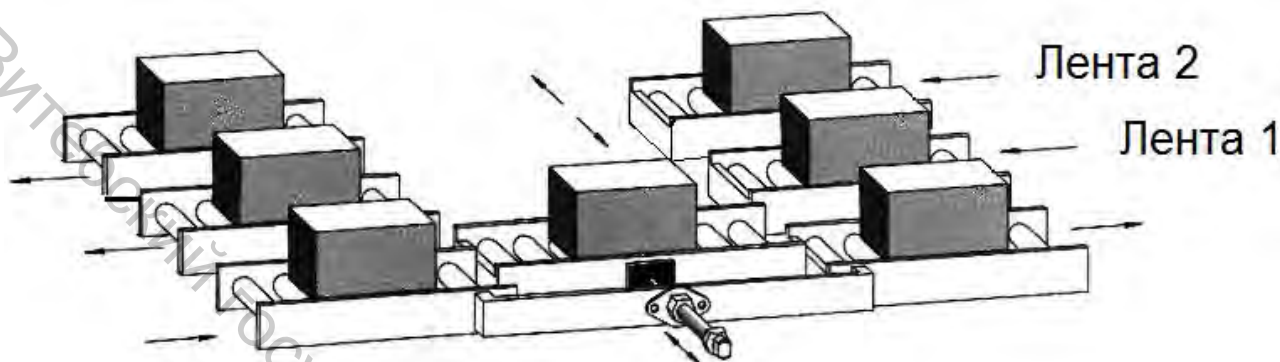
Эскиз устройства перемещения заготовок
